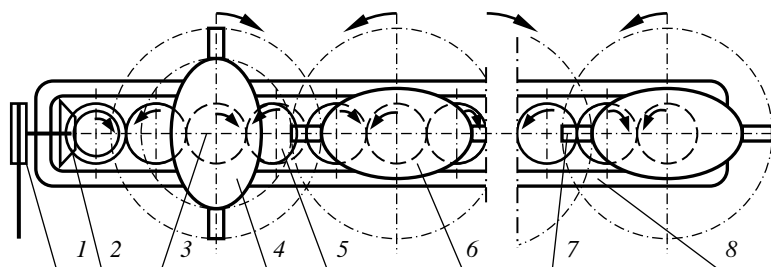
Кинематическая схема многороторного рабочего органа с боковым приводом: 1 – привод; 2 – конический редуктор; 3 – ведущая шестерня; 4 и 6 – диски; 5 – промежуточные шестерни; 7 – ножи; 8 – корпус
